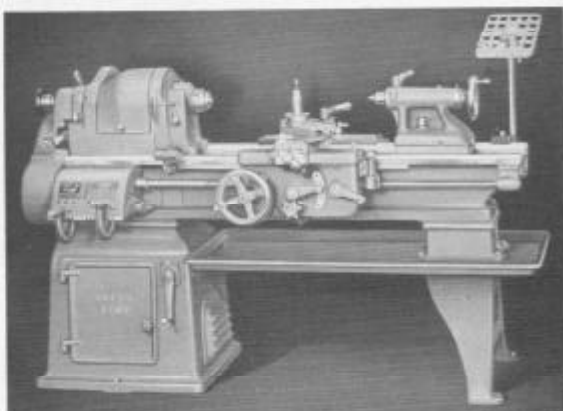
Torno moderno para taller con transmisión por motor debajo del cabezal
